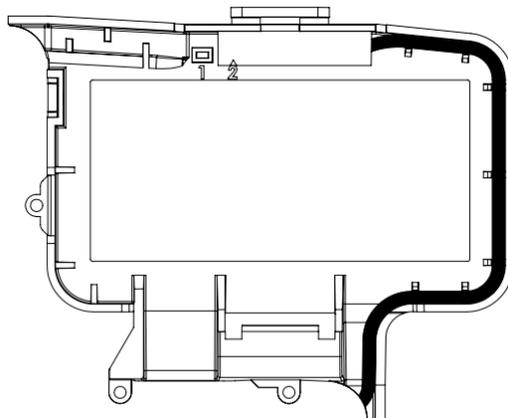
Montaje superior del adaptador (superposiciones) al grabador MacR6 (se requieren 2 tornillos TORX T10 adicionales 3x1)
